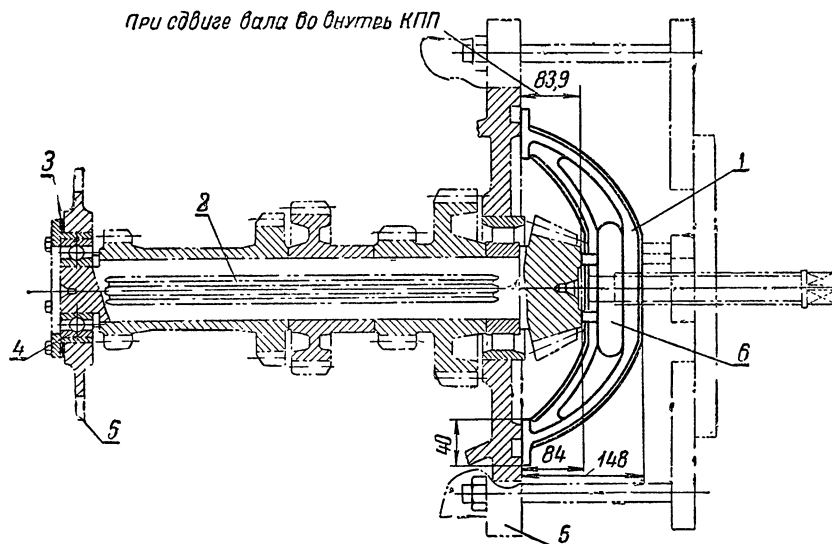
Установка нижнего вала коробки передач по шаблону:
